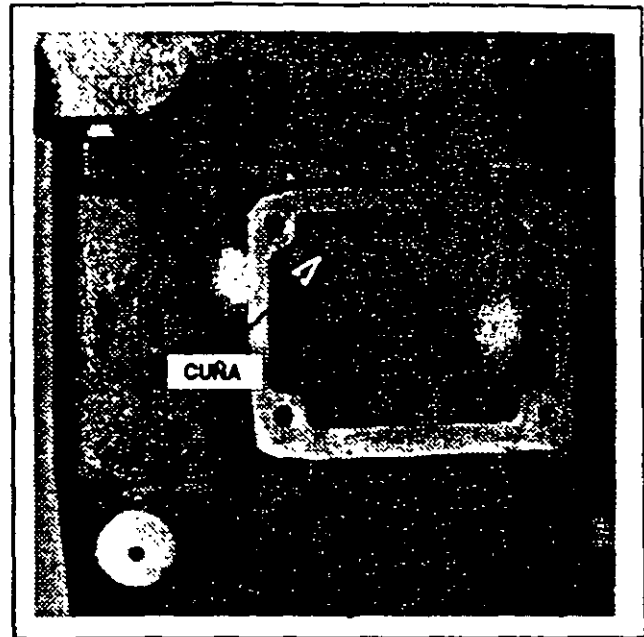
"CUÑA" SOLDADA EN LA ABERTURA
